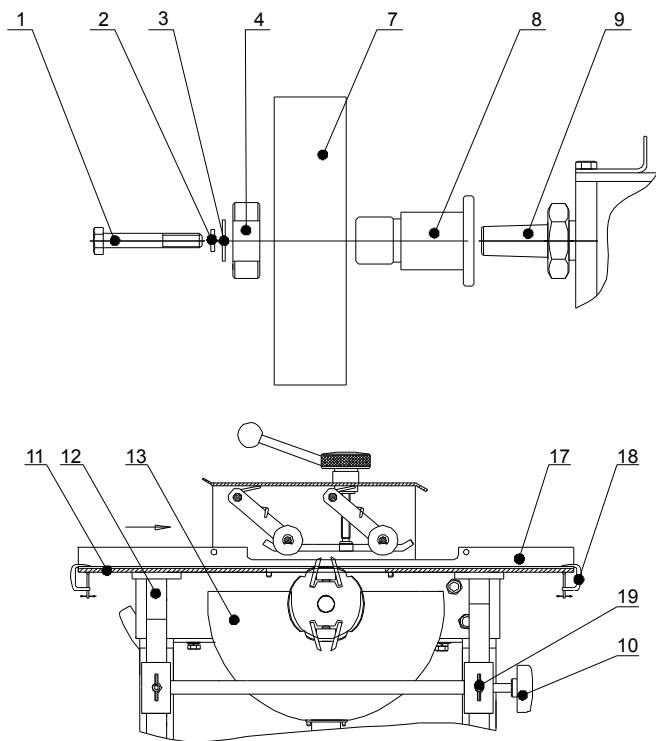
Фрезерование дисковыми и фасонными фрезами
